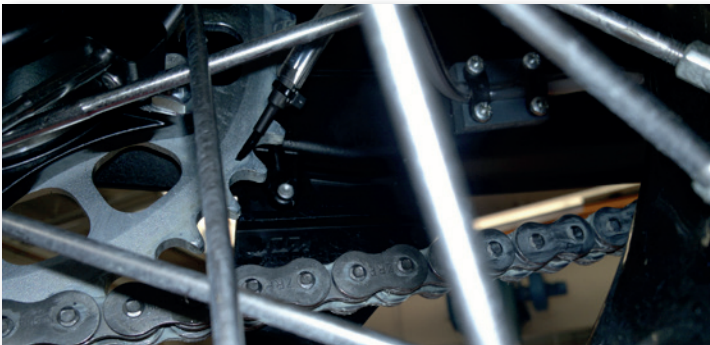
Falsche Düsenposition: die Düse ist zu weit vom Auflaufpunkt der Kette auf das Kettenrad entfernt.
